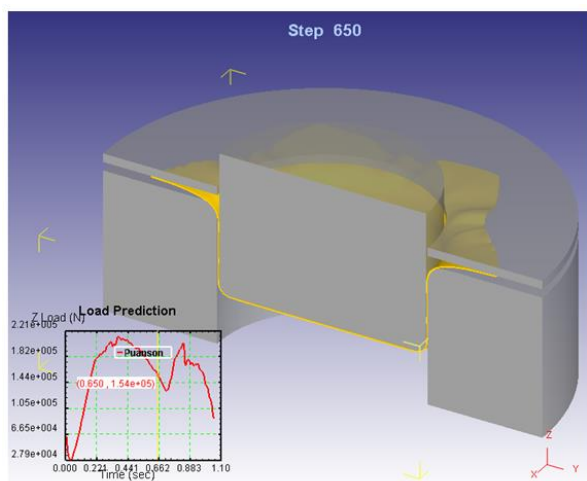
Вытяжка квадратной заготовки модель в разрезе
